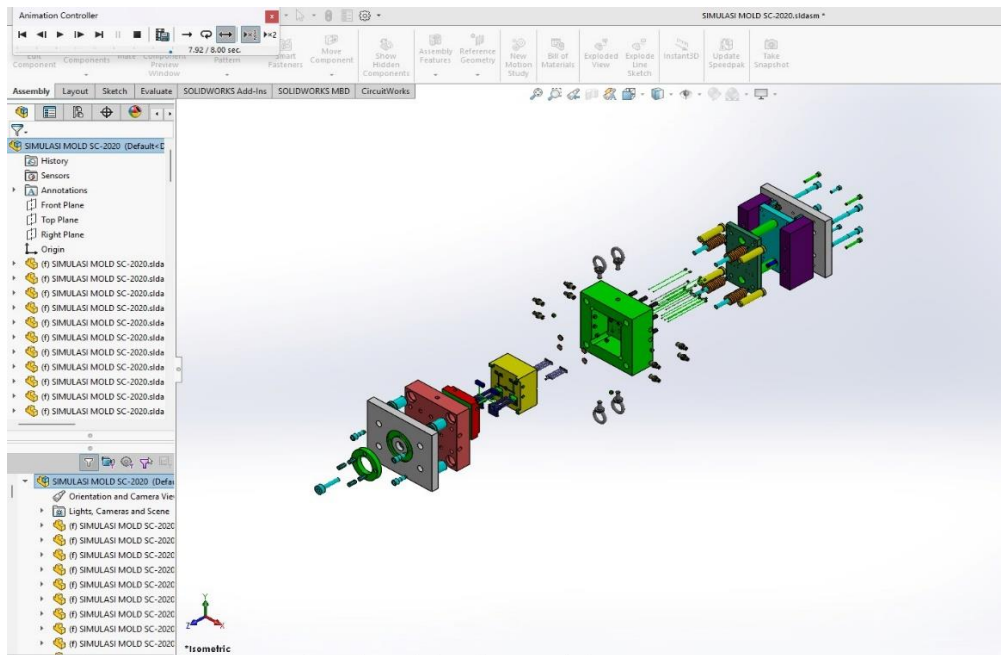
Proses Assembly Desain Cetakan Produk *Holder
